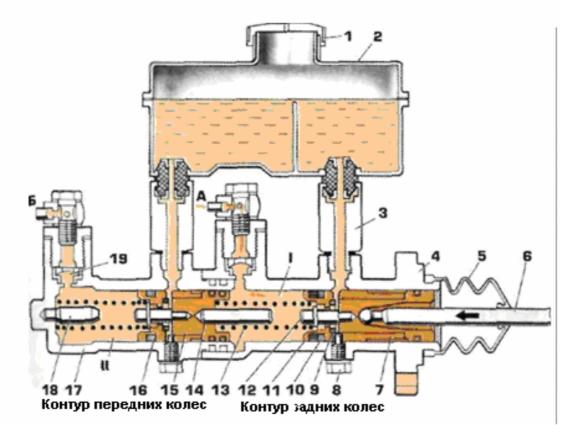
Главный тормозной цилиндр автомобиля ГАЗ
